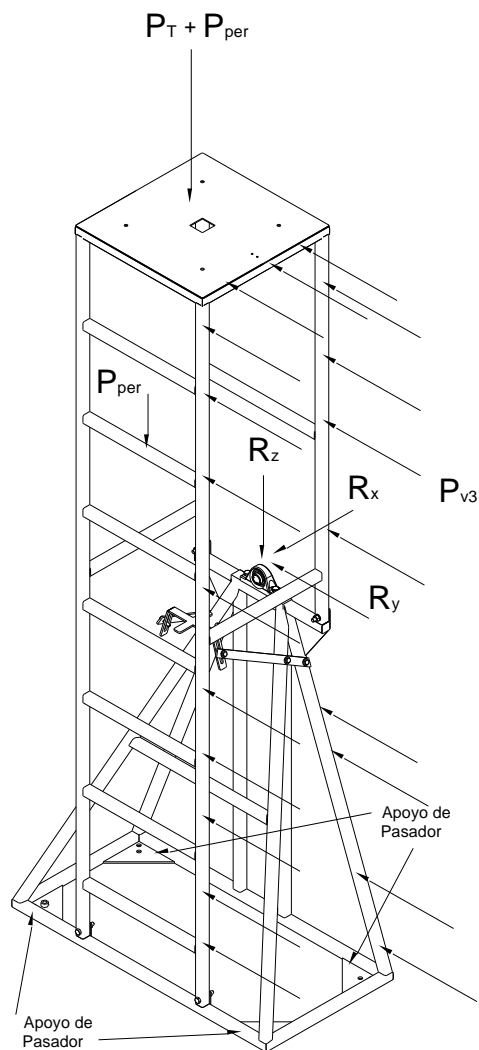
Cargas y tipos de apoyo que actúan en la estructura base.
